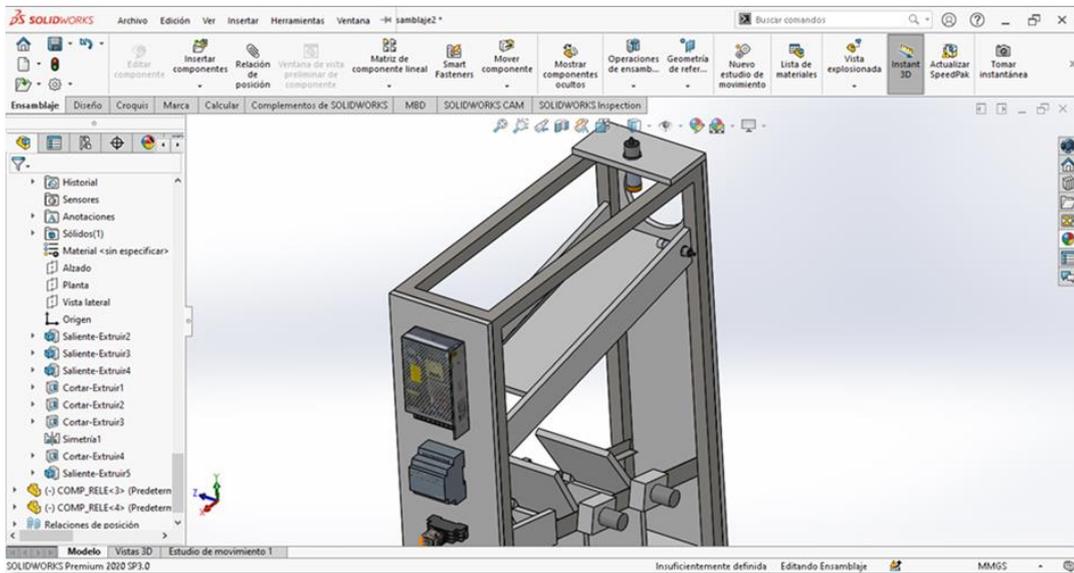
Proyecto ensamblaje – Solidworks (Vista 3)
